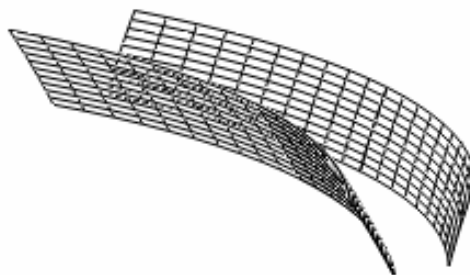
Компьютерная модель рабочей поверхности арочного зуба-перемычки
